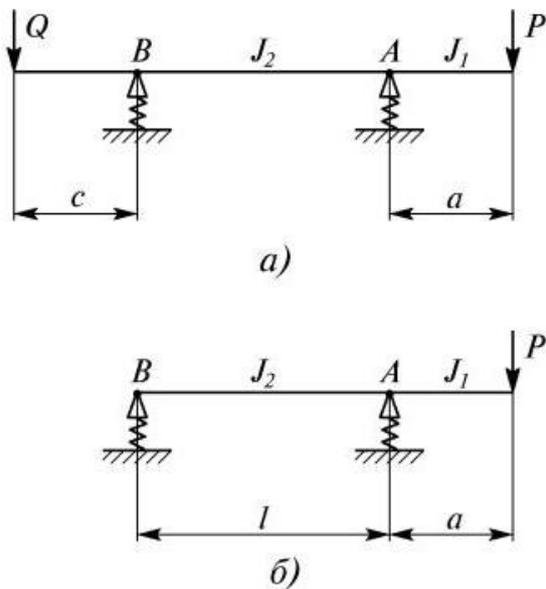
Схемы расчета шпиндельного узла на жесткость
